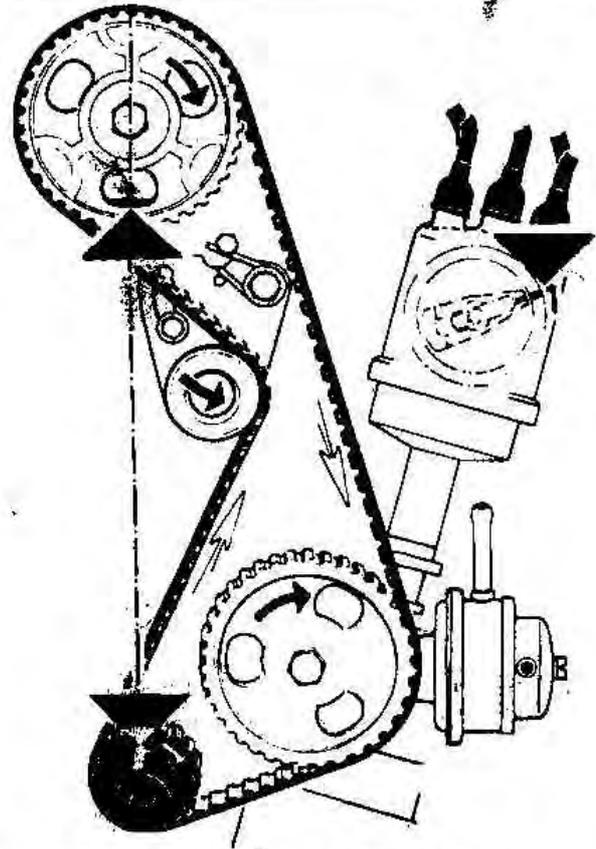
Б.17. Регулировка зубчатого ремня (Разд.59)
